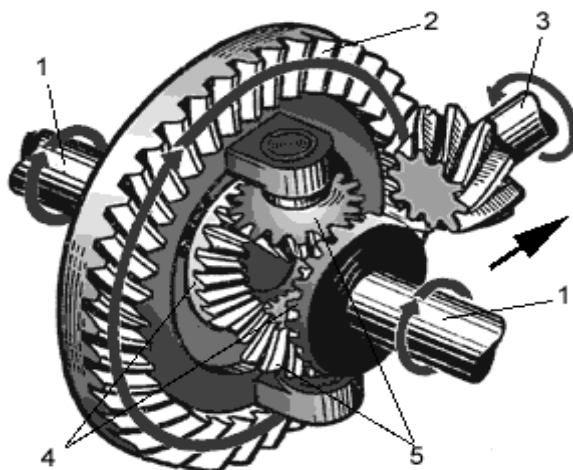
Главная передача с дифференциалом 1 - полуоси; 2 - ведомая шестерня; 3 - ведущая шестерня; 4 - шестерни полуосей; 5 - шестерни-сателлиты
